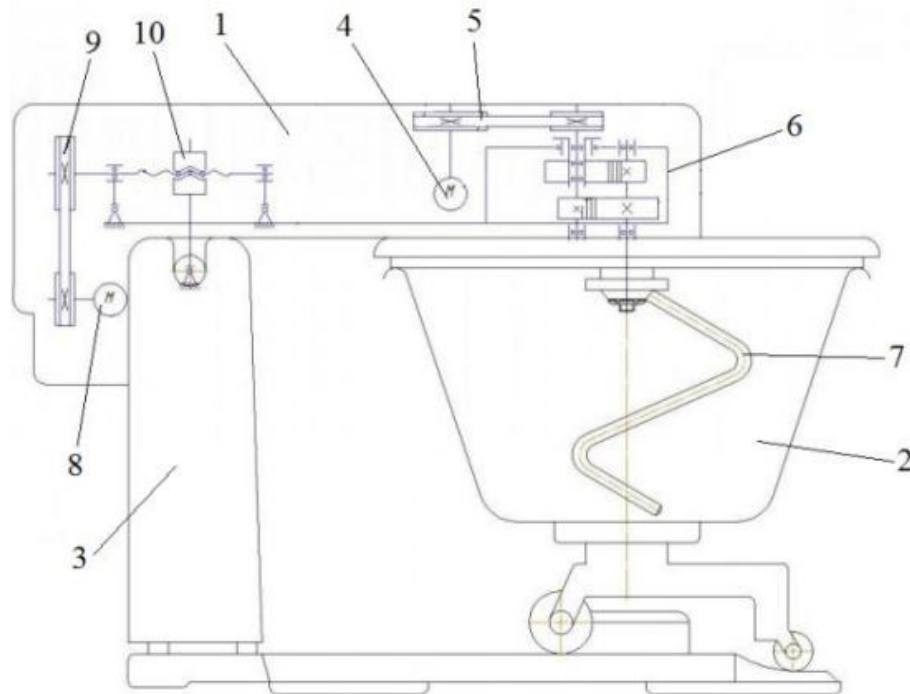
Машина тістомісильна ТММ-140: 1 - рухома траверса; 2 - дежа; 3 - станина; 4 - електродвигун; 5 – механізм приводу; 6 - планетарний редуктор; 7 -спіральні робочий орган; 8 - електродвигун; 9 - привід; 10 - робочий механізм
